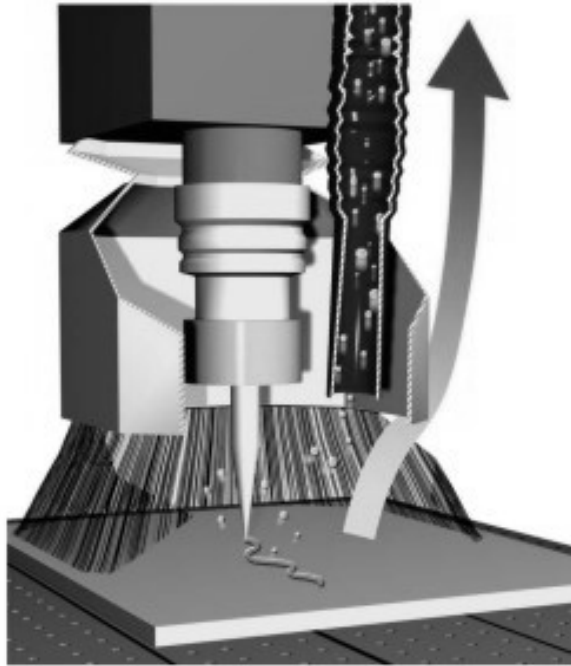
Автоматичний фартух для видалення стружки
